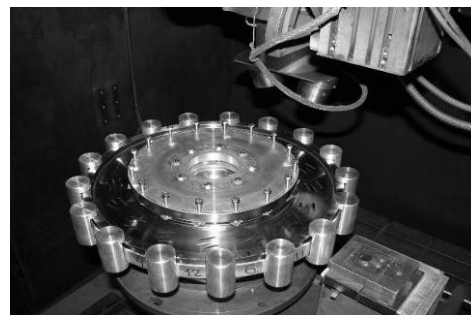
Внешний вид прототипа опытного диффузора, собранный под сварку в приспособлении
